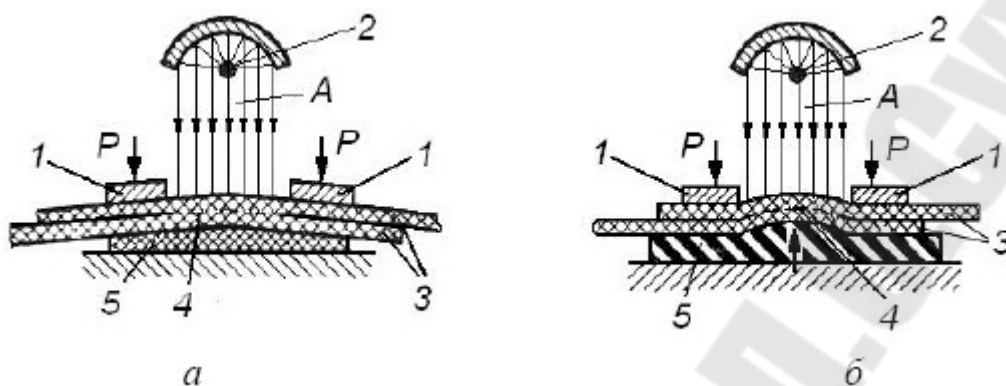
Схема сварки инфракрасным излучением:
